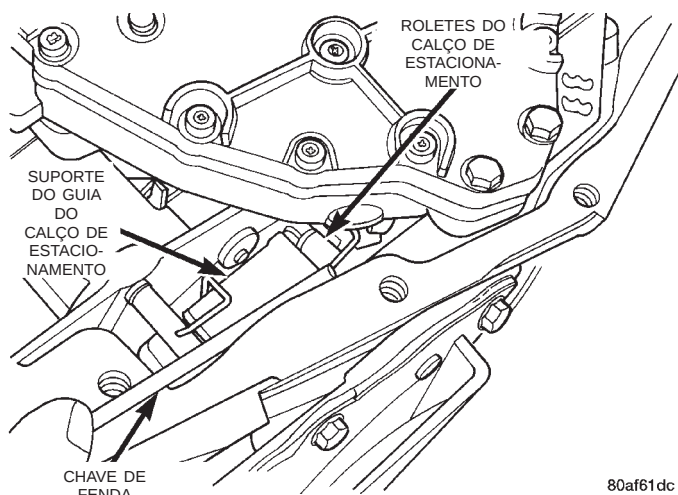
Remoção dos Roletes da Haste de Estacionamento do Suporte da Guia
